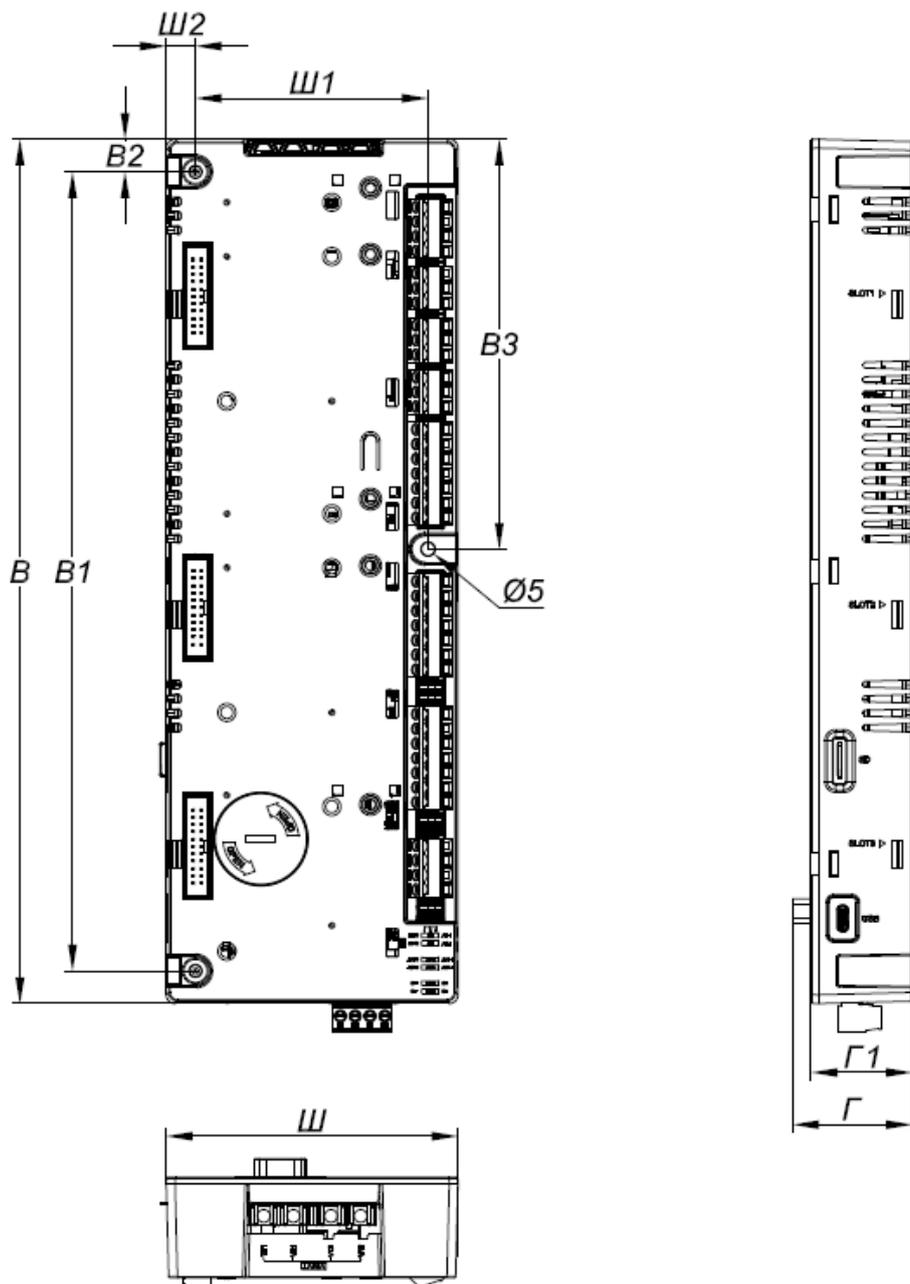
Габаритный чертеж модуля управления
